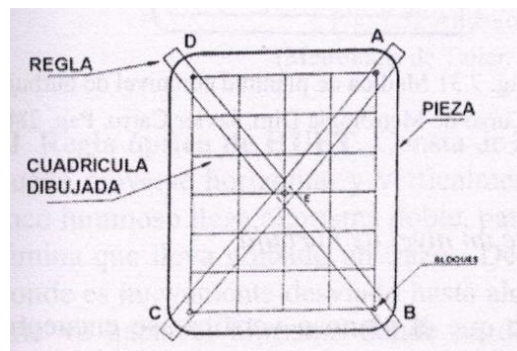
Control de planitud con regla y bloques patrón [5]
